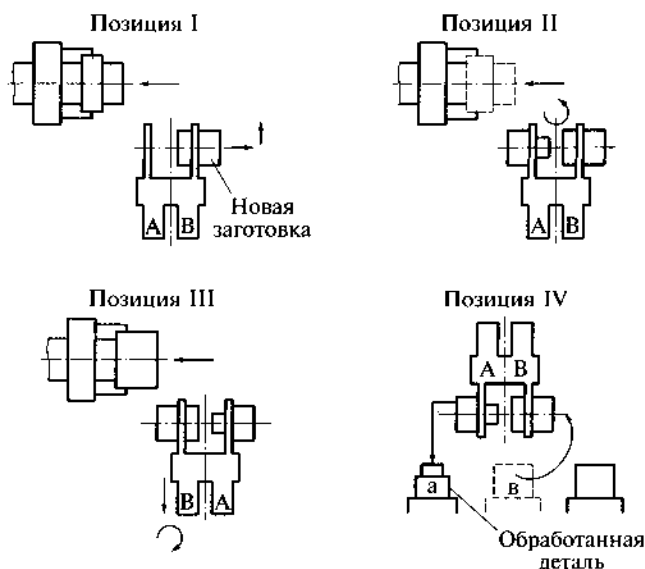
Схема работы ГПМ на базе токарного станка и робота с двумя схватами
